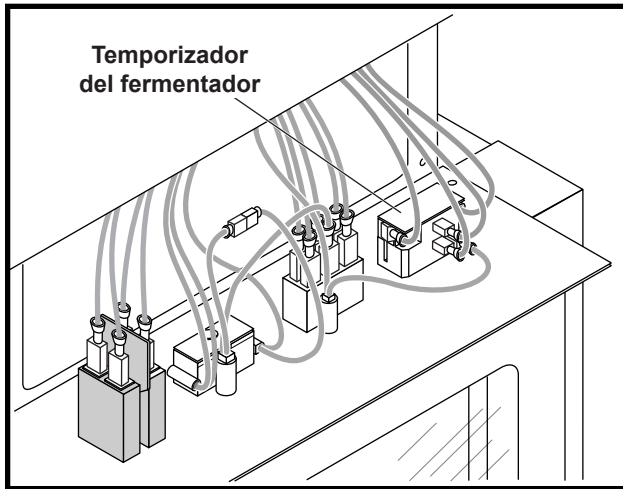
Conexiones de los elementos calefactores del fermentador – Parte trasera izquierda
